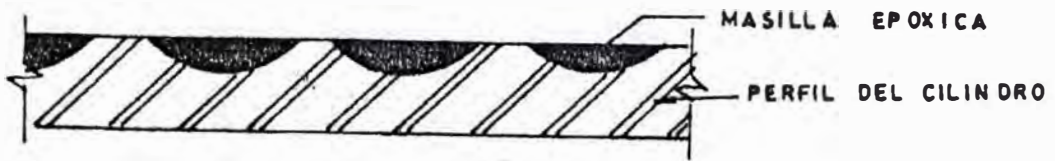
DETALLE DE APLICACION DE MASILLA EPOXICA
